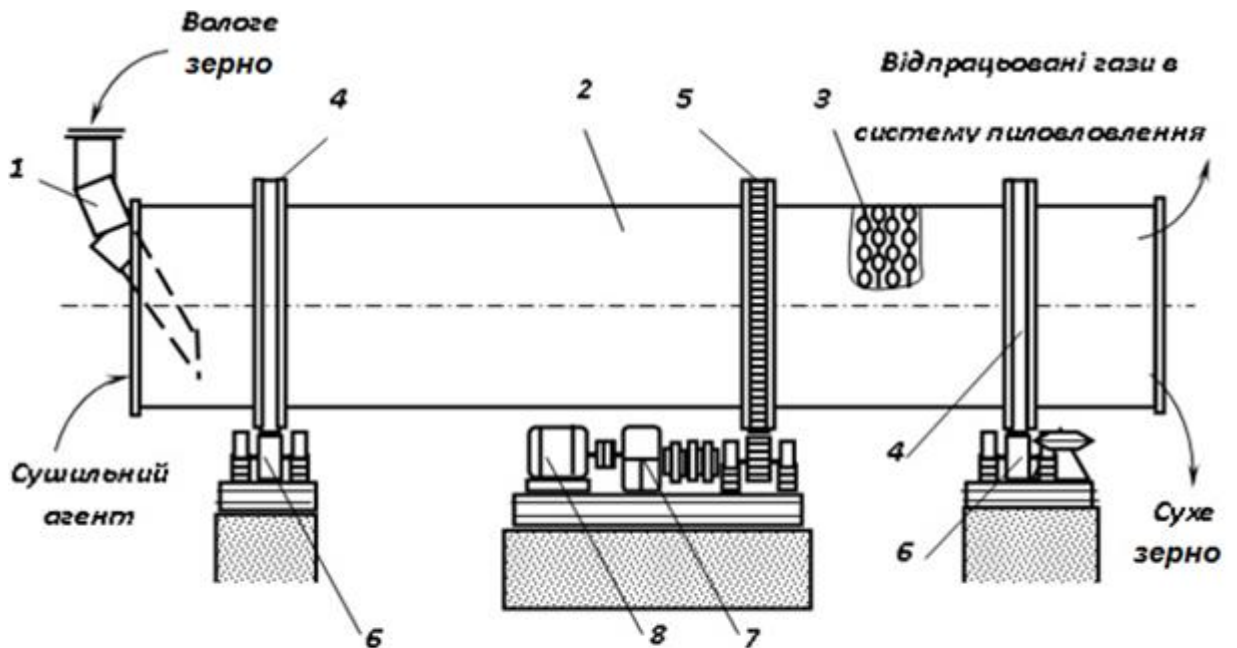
Барабанна сушарка. 1 – завантажувальний лоток; 2 – барабан; 3 – ланцюгові насадки; 4 – бандаж; 5 – привідна вінцева шестерня; 6 – котки; 7 – редуктор; 8 – електродвигун.
